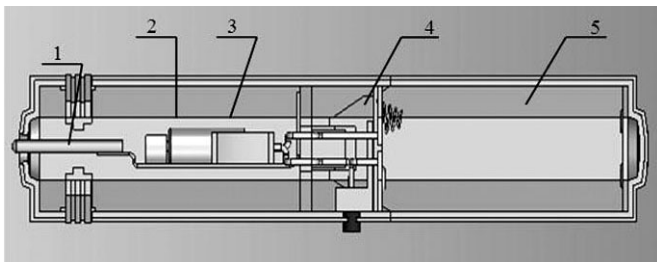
Устройство для неинвазивной диагностики состояния кожного покрова (вид сбоку без корпуса)
